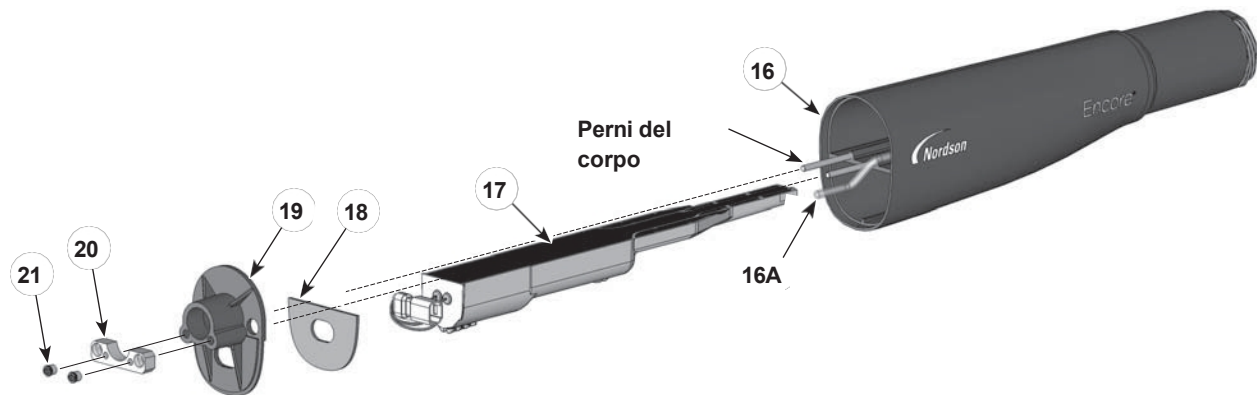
Smontaggio della pistola - Sostituzione dell'alimentatore
